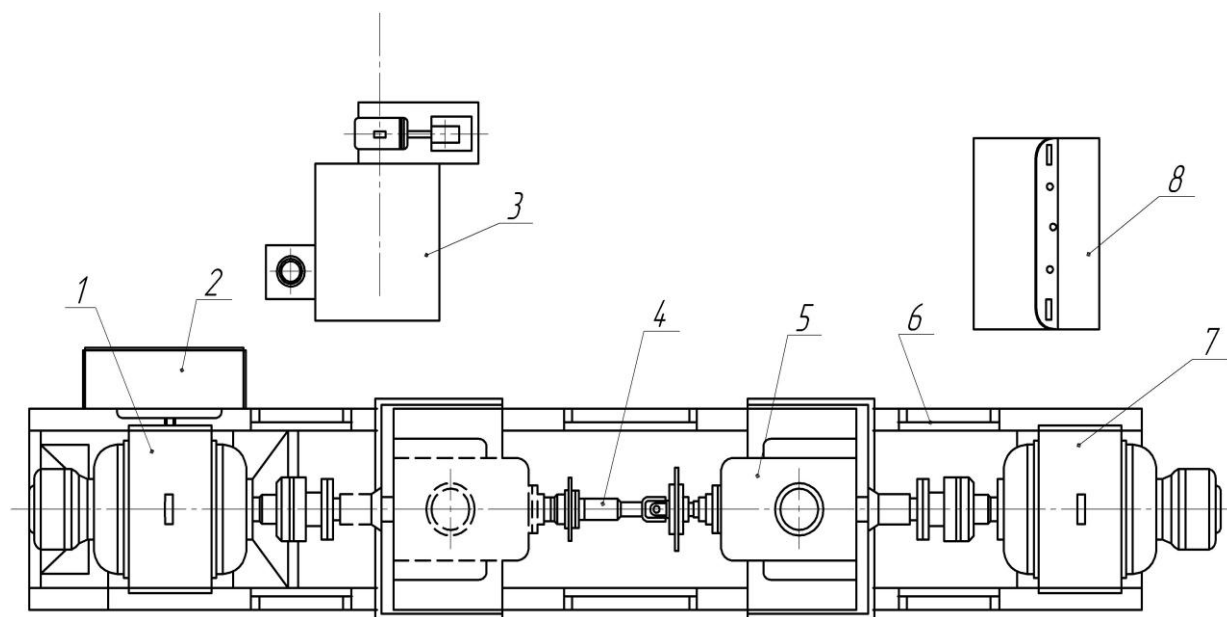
Стенд для испытания коробок передач, модель 6101-11
